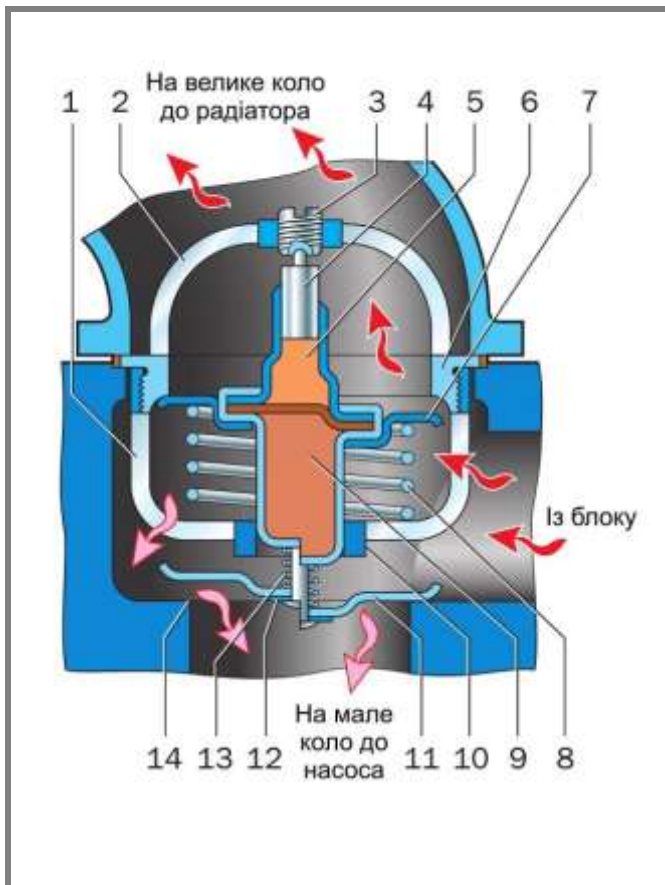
Будова термостата з твердим наповнювачем: 1, 2 – нижня і верхня рамки; 3 – регулювальний гвинт; 4 – шток; 5 – гумова буфер-мембрана; 6 – сидло основного клапана; 7 – основний клапан; 8 – пружина; 9 – капсула; 10 – направляюче кільце; 11 – перепускний клапан; 12 – пружне кільце; 13 – підтискна пружина; 14 – сидло перепускного клапана
